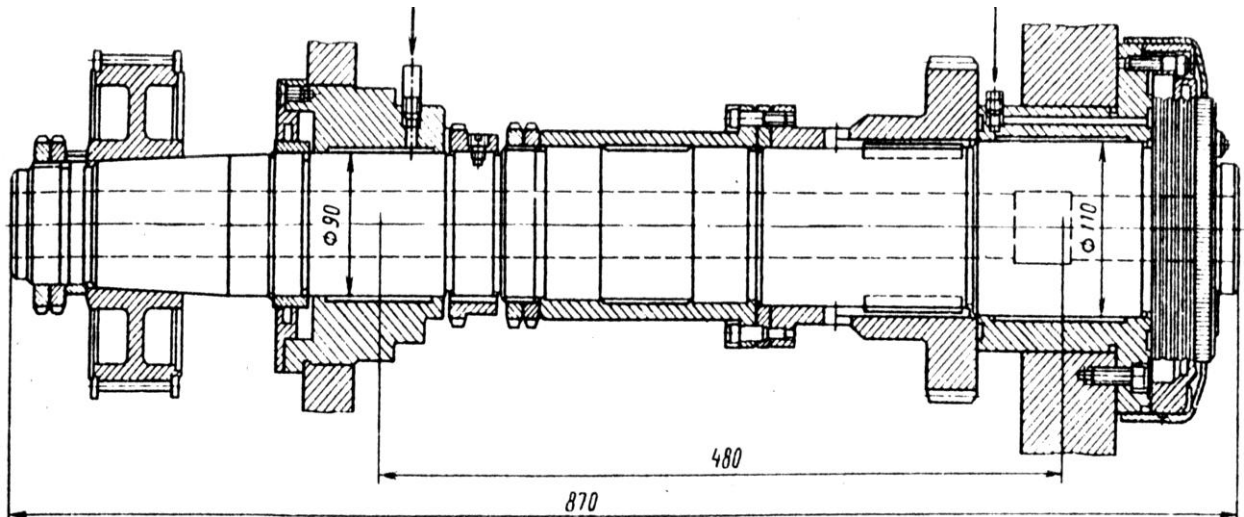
Шпиндель з ГСП прецизійного токарно-гвинторізного верстата
